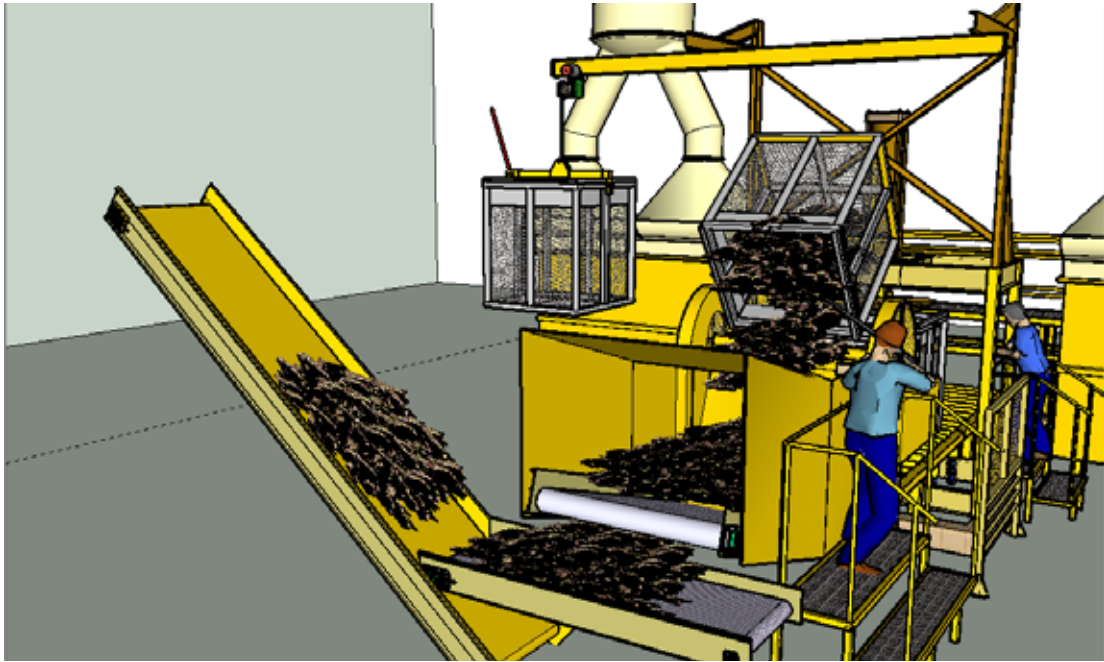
Imagen N° 3 del Dispositivo Propuesto
